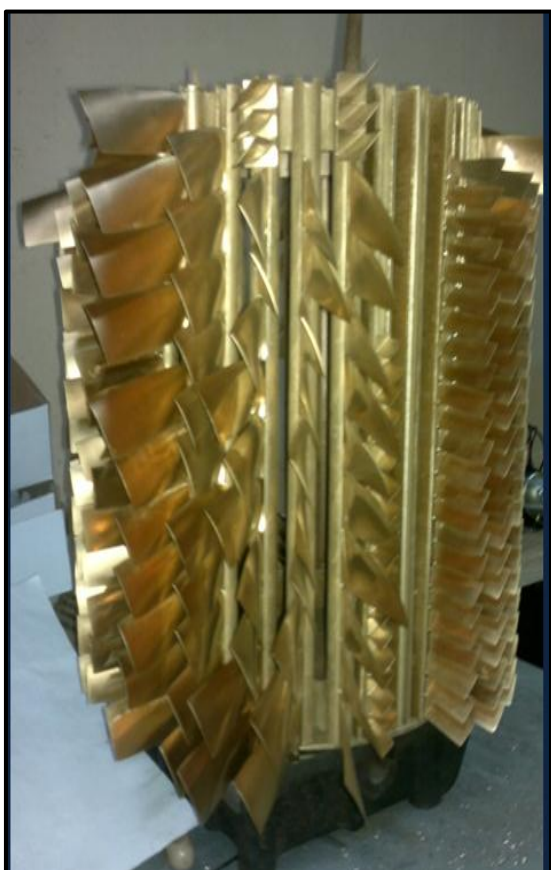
Общий вид цилиндрической оснастки вакуумной камеры для напыления рабочих лопаток компрессора ГТП
